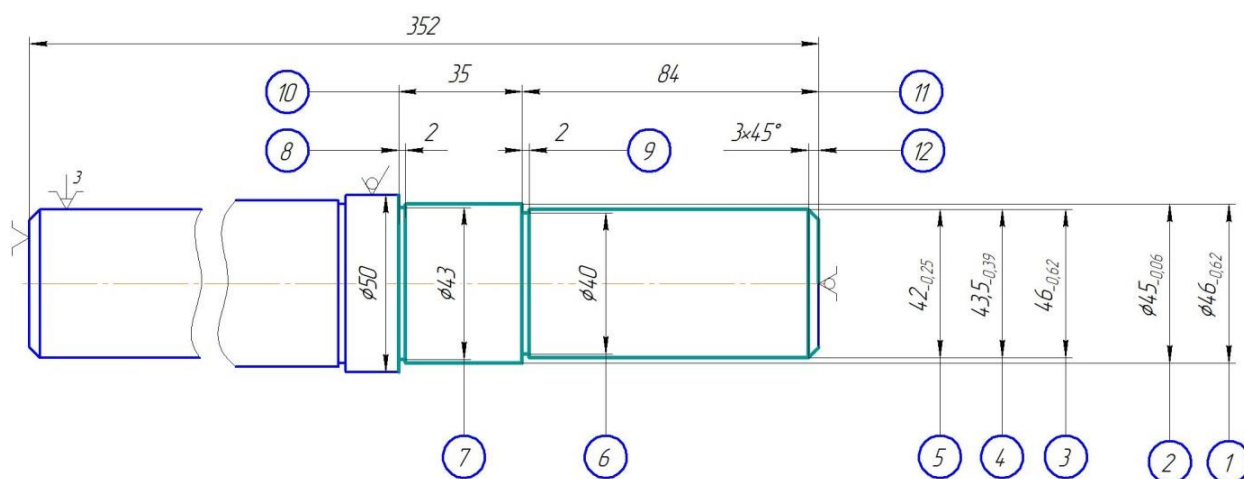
Эскиз операции 020 Токарная с ЧПУ детали Вал
